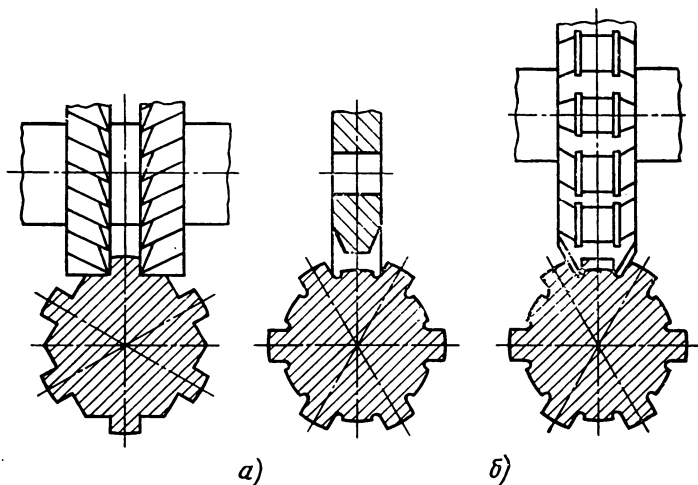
Методы обработки зубьев вала дисковыми профильными фрезами
